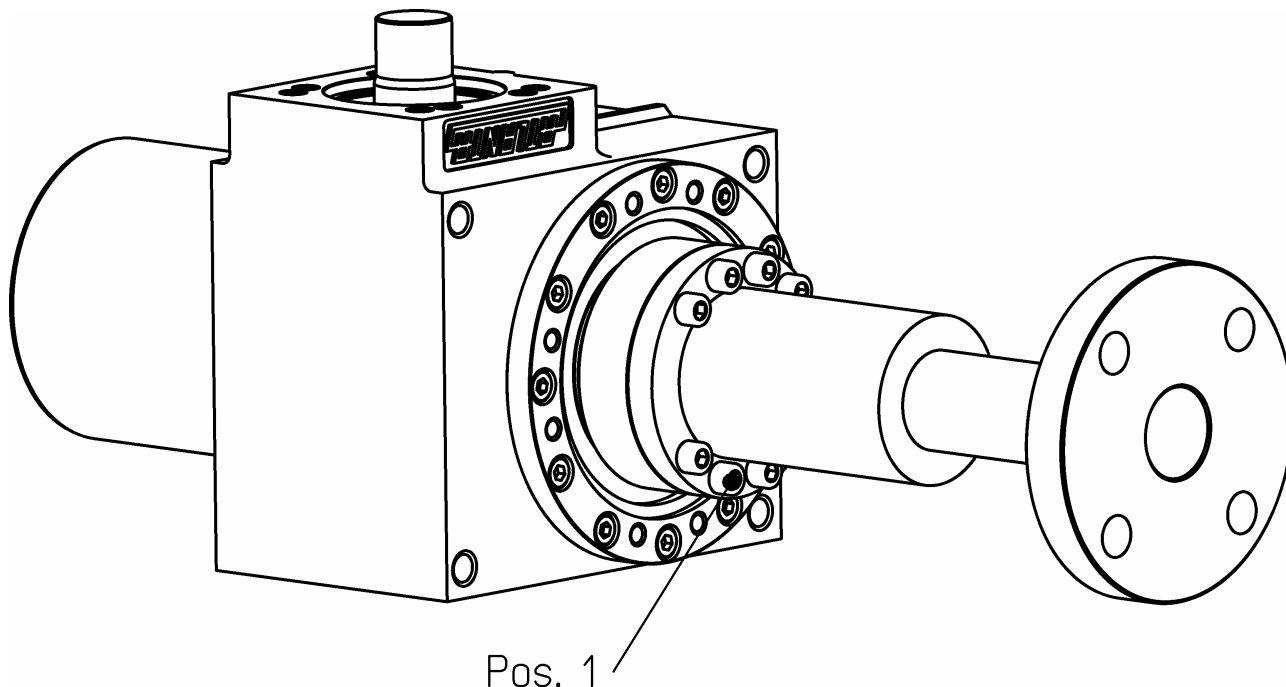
Spindelwechsel bei Getrieben mit stehender Spindel
